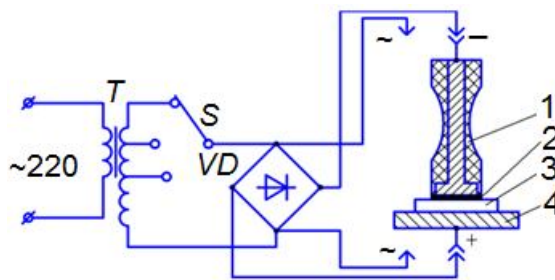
Схема установки для електрохімічного маркування : 1 – електрод-інструмент; 2 – трафарет; 3 – виріб; 4 – робочий стіл
